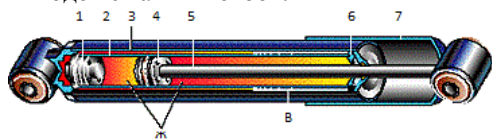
Схема гидравлического двухтрубного амортизатора: 1- клапан сжатия; 2 — рабочий цилиндр; 3 — цилиндр резервуара; 4 — поршень и клапан отбоя; 5 — шток; 6 — уплотняющий и
